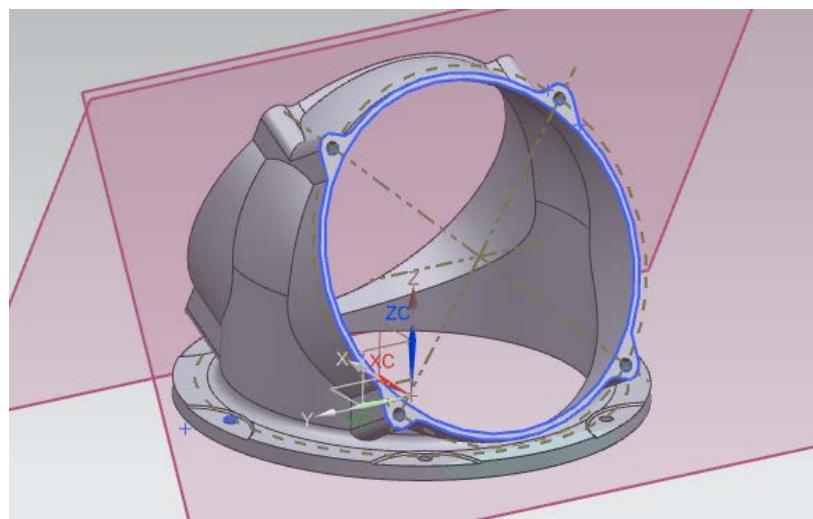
3D модель корпуса с резьбовыми отверстиями на фланцевых частях
